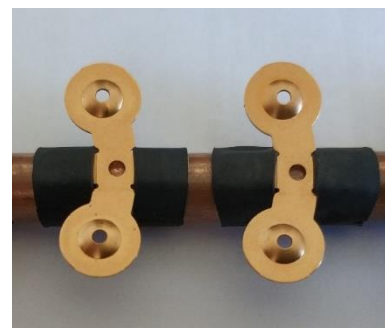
Exemple punt de soldadura terminals amb busbar.
